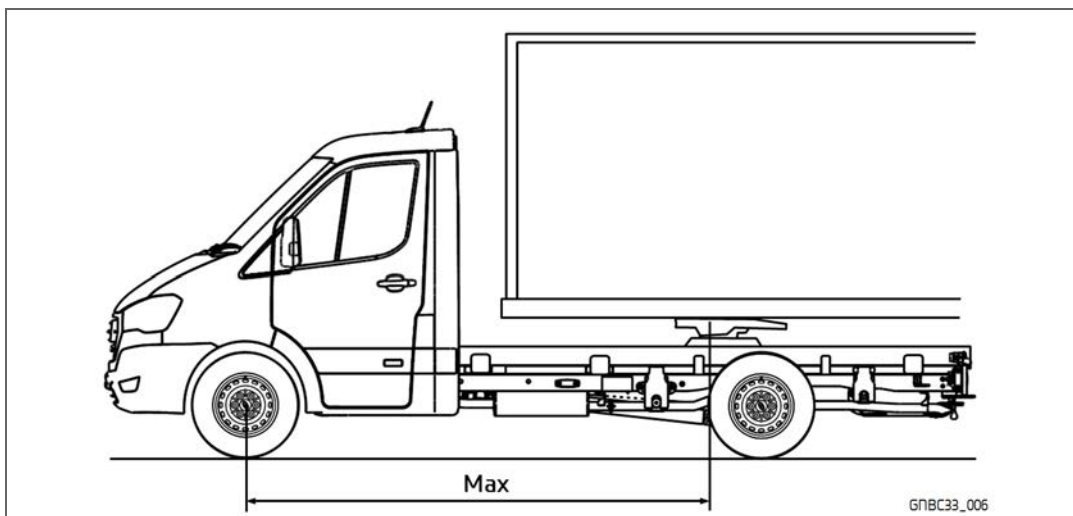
Hauptabmessungen des Aufliegers und Spaltmaße
